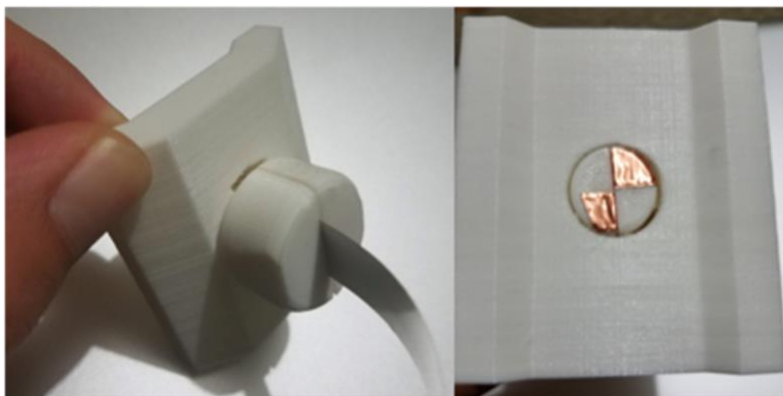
Ensamble final del mecanismo de giro-cierre entre las tapas, el sensor y la torre base
